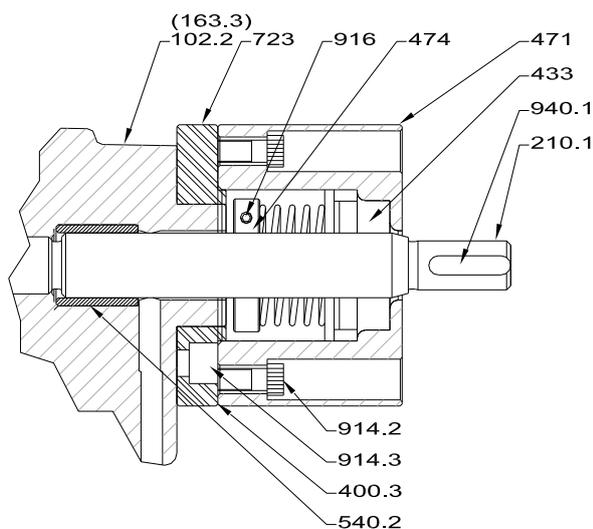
Desenho em Corte bomba FBE c/ selo mecânico
